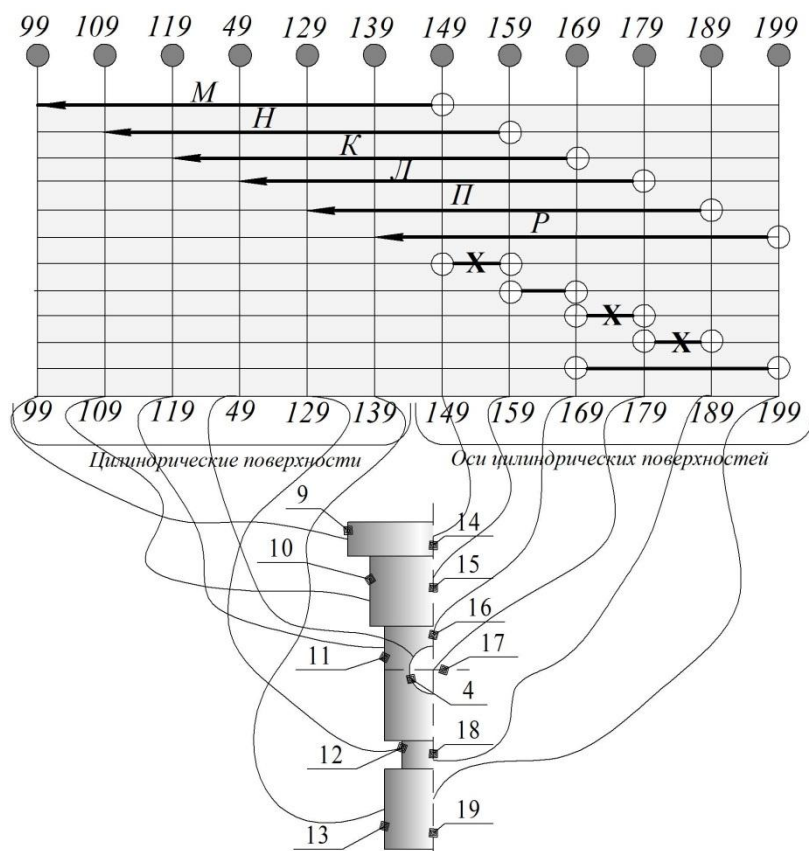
Преобразованный чертеж детали (вторая проекция)
